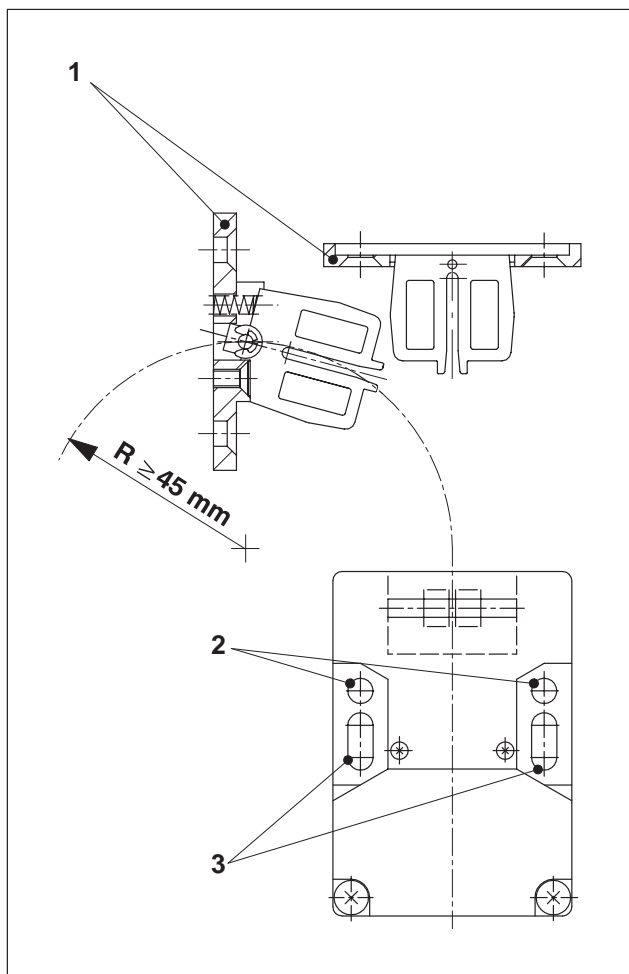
Schlüsselschalter mit beweglichem und starrem Schlüssel
